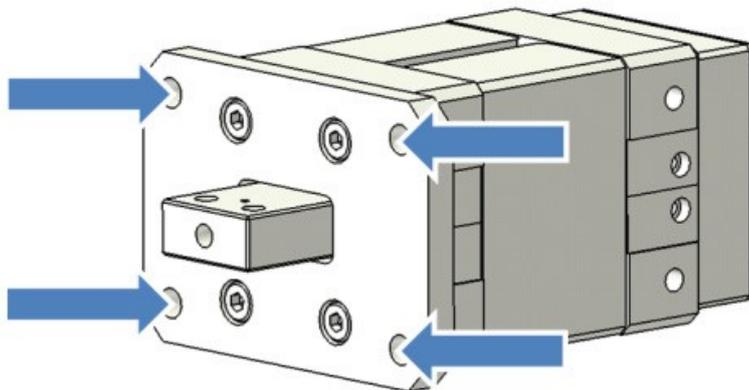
Montageflansch B: Position der verwendeten Montagebohrungen
